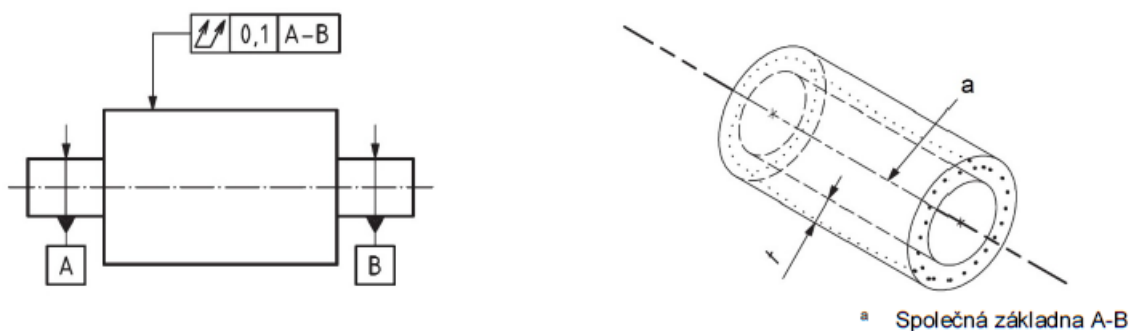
Indikace tolerance axiálního házení [14]
